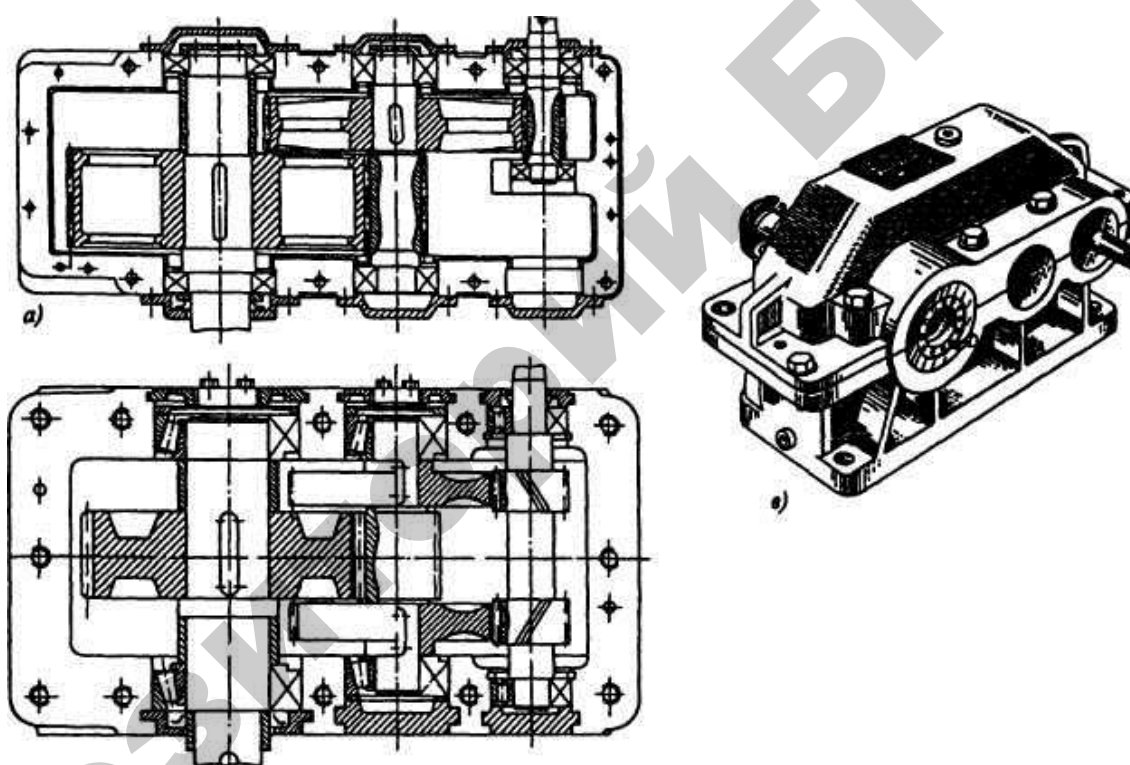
Двухступенчатый зубчатый редуктор:
